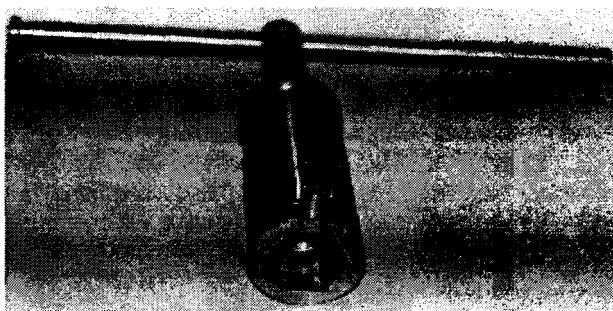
Ключ для демонтажа ведущих колес грузовых автомобилей ЗИЛ и ГАЗ
